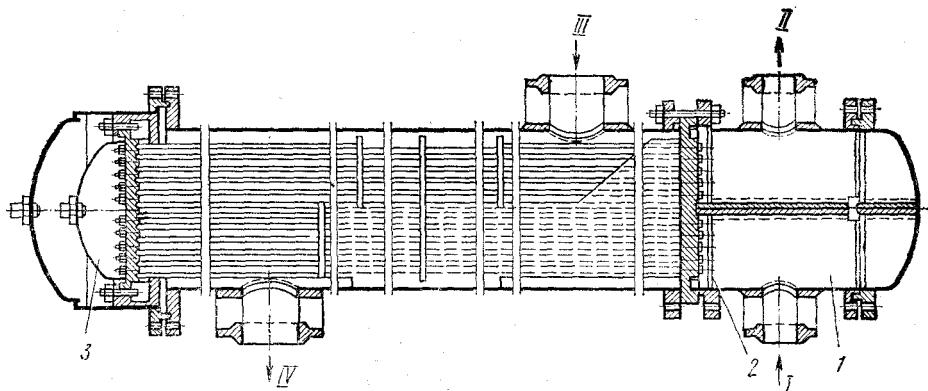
Схема двухходового кожухотрубчатого теплообменника с плавающей головкой:
